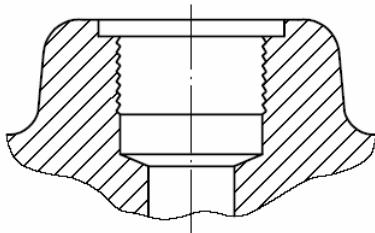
Ответный торец для удержания прокладки, если используются цилиндрические резьбы
